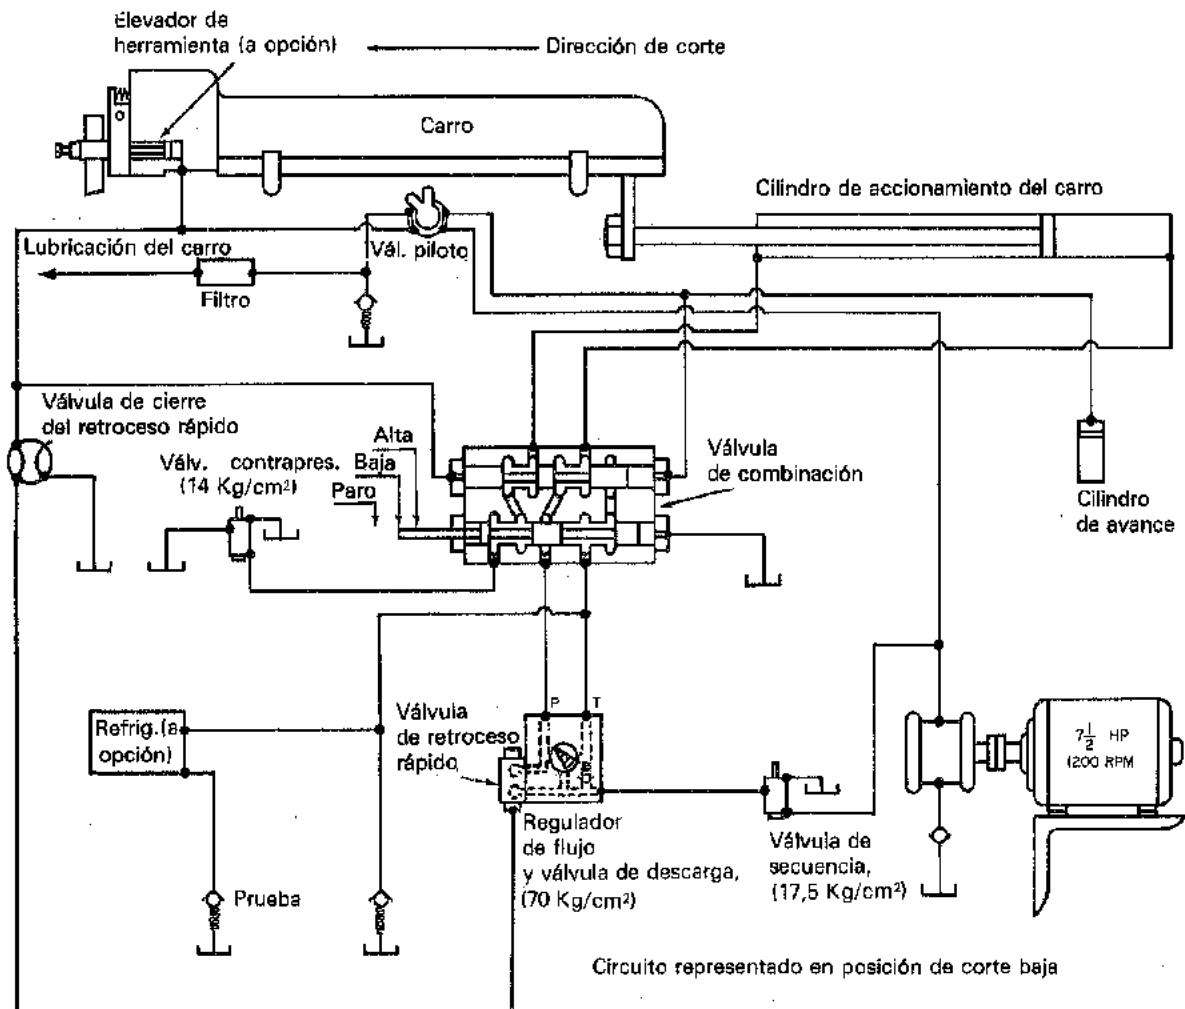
Circuito hidráulico de la limadora hidráulica Rockford (Rockford Machine Tool Co.)
